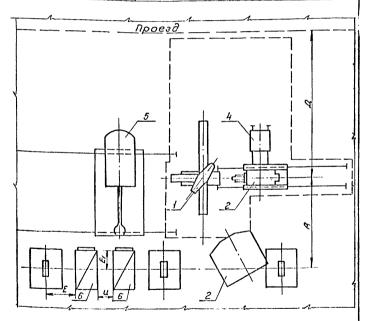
Схема расположения участка автоматизированного ковочного комплекса. 1-гидравлический ковочный пресс. 2-пульт управления. 3-ковочный манипулятор. 4-тележка с поворотным столом, 5-шаржир-машина. 6-Печи нагревательные камерные.
